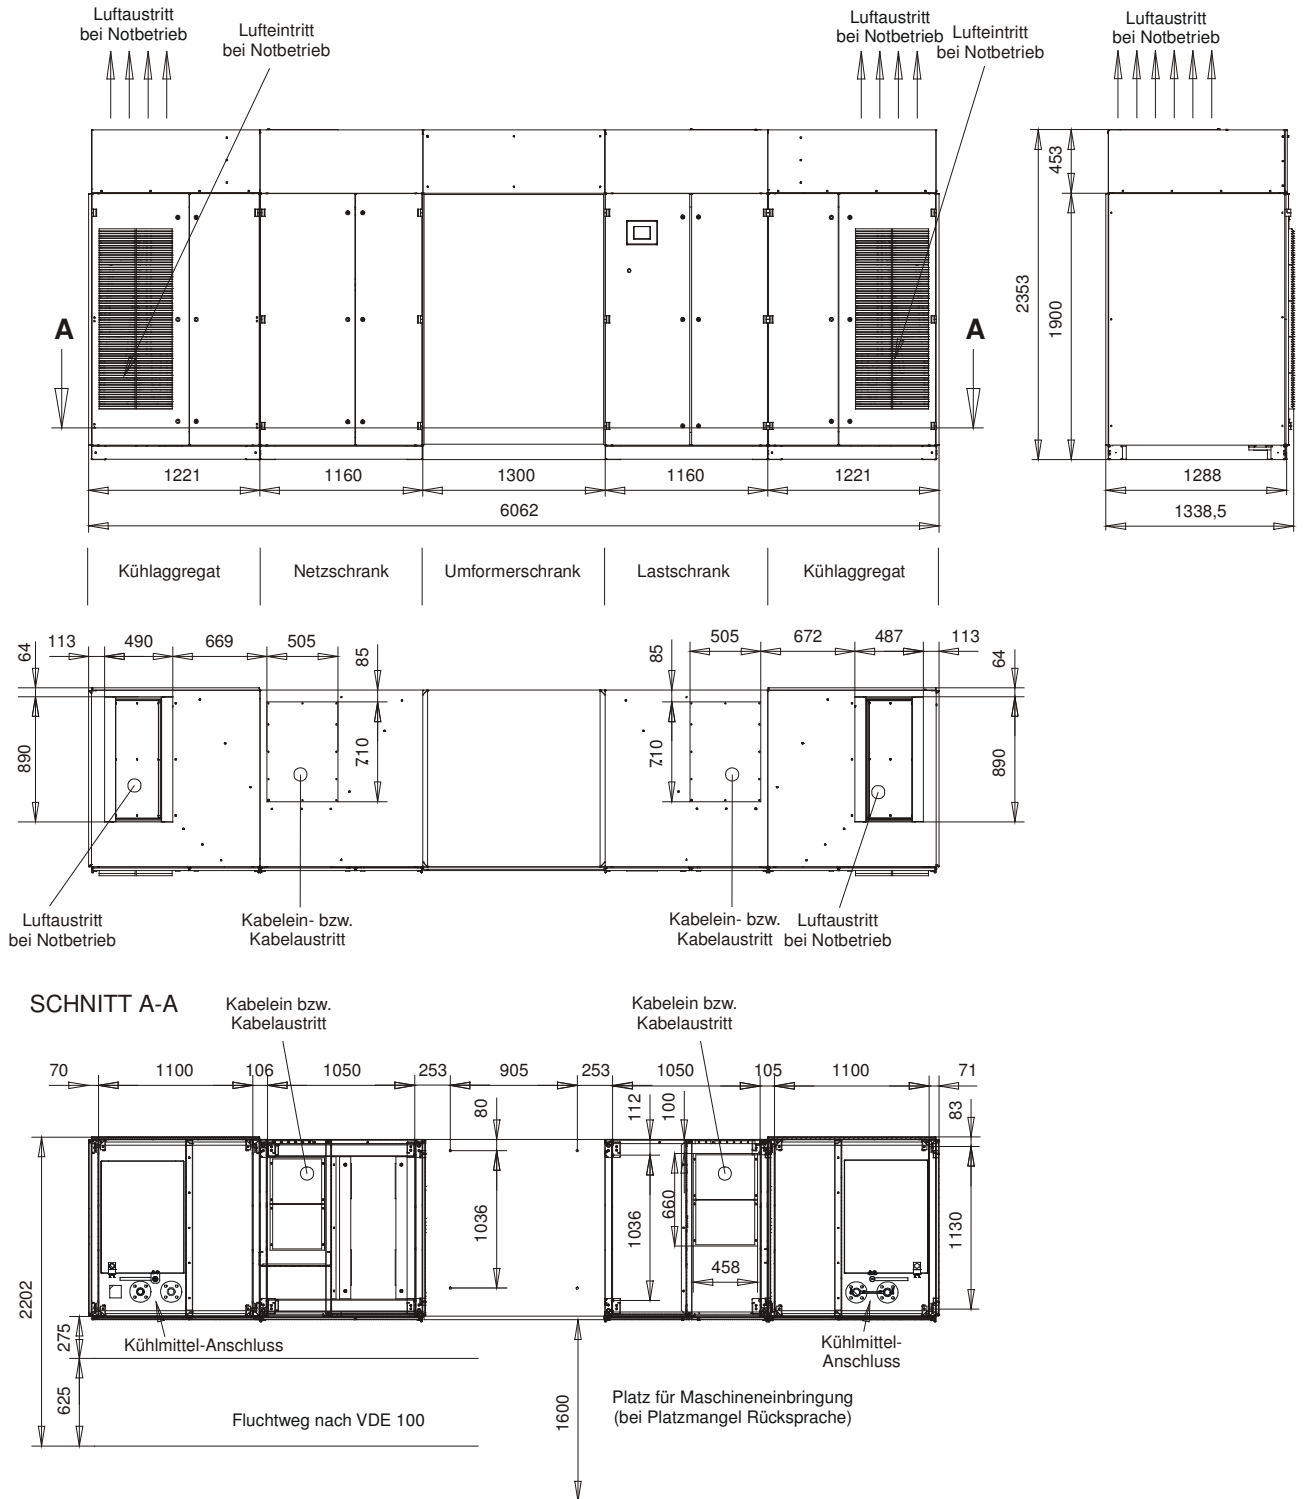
Abmessungen UB800 – UB1100 mit Wasserkühlung
